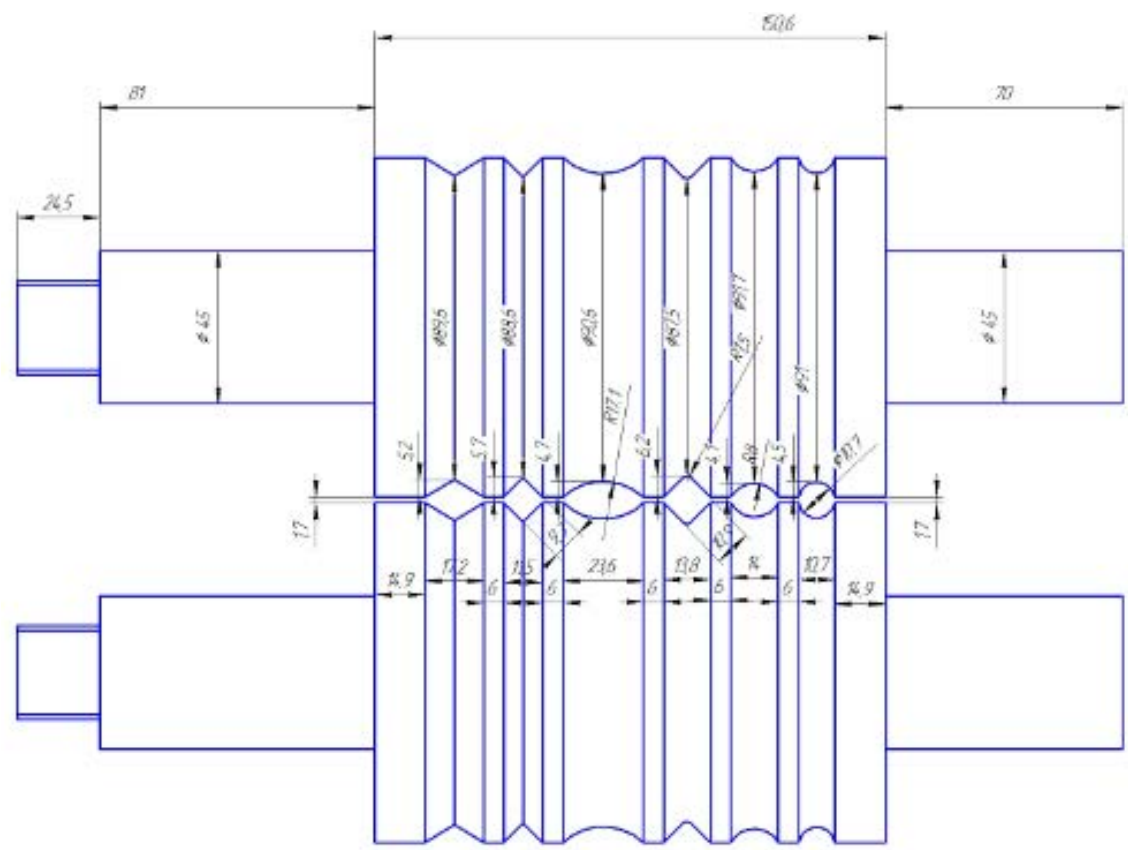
Калибровка валков стана 100 для прокатки простых профилей
